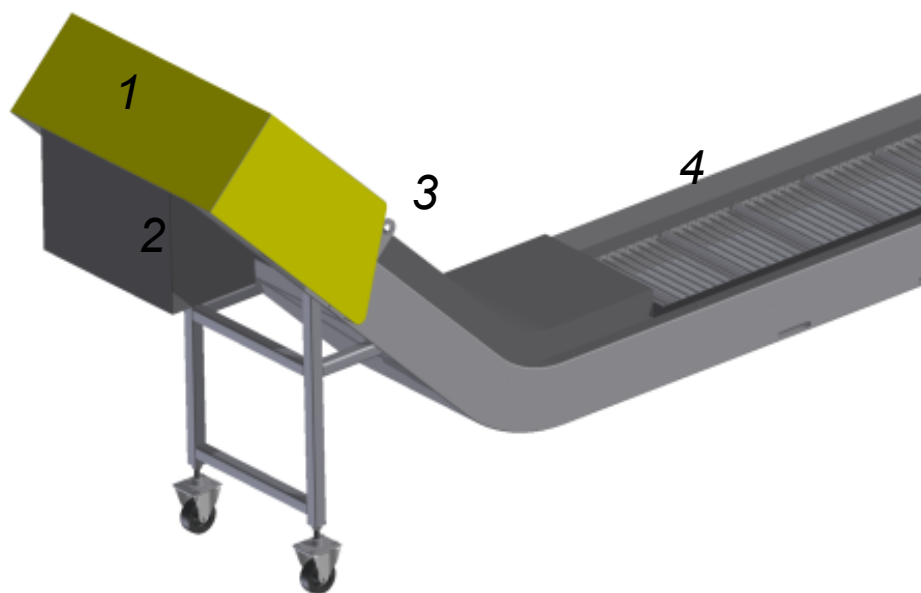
Detail směru průtoku chladicí kapaliny
